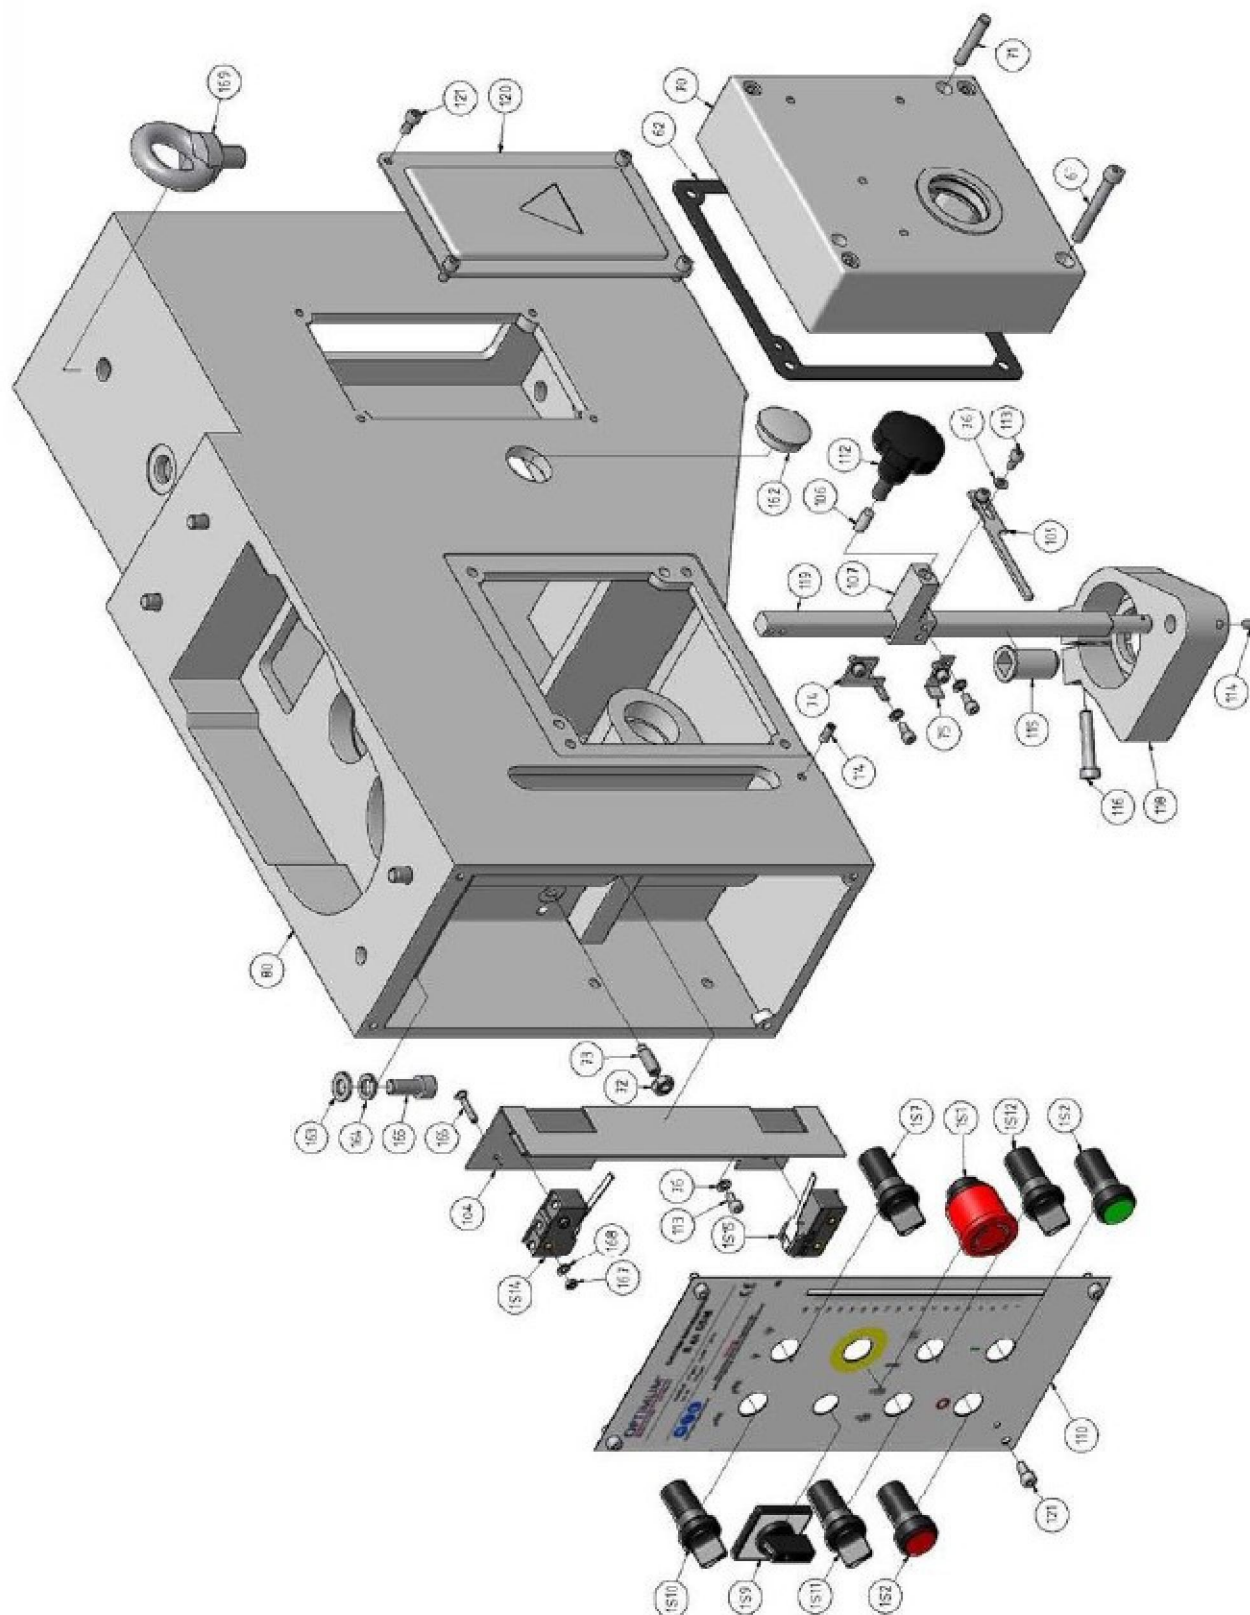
Caja de engranajes de avance 3 de 4 - Feed gear box 3 of 4
